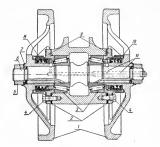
Регулировка подшипников опорных катков тракторов ДТ-54, ДТ-54А и Т-75:
